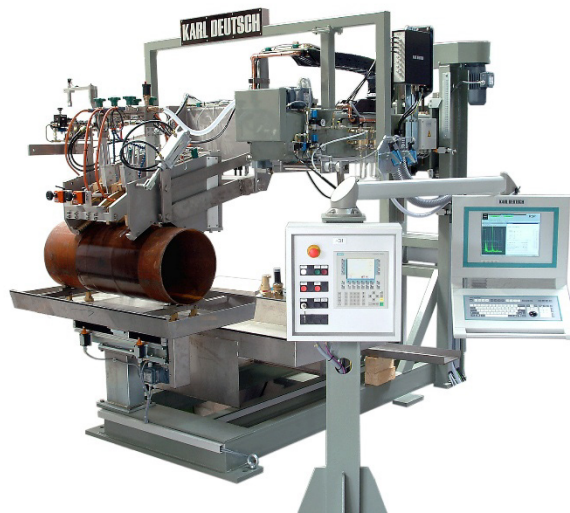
Schweißnahtprüfanlage in klassischer Bauform mit Ausleger
